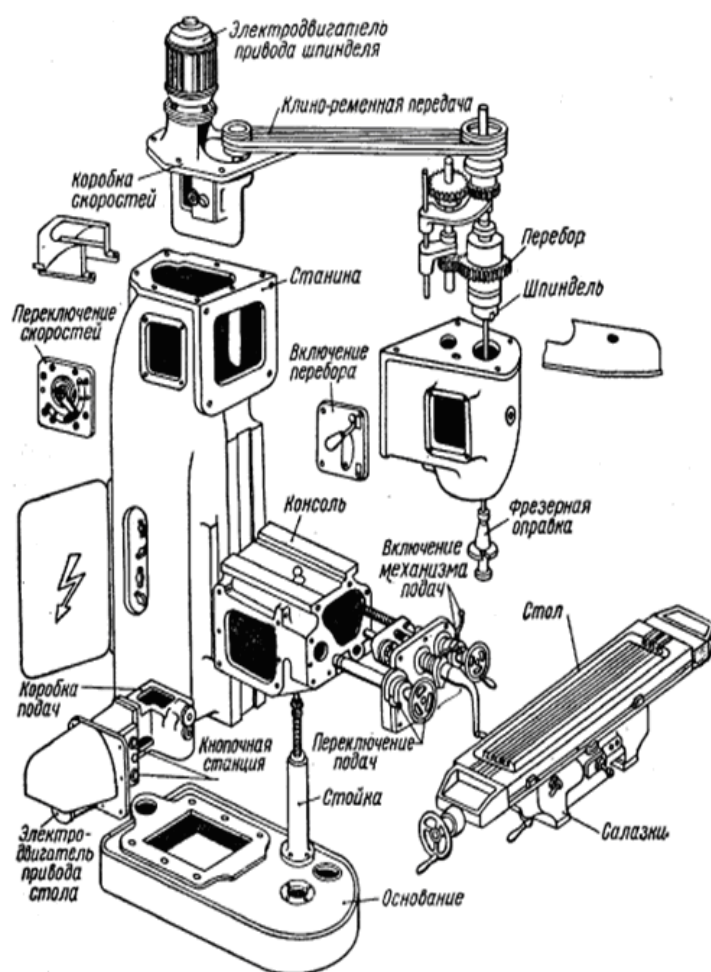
Основные узлы консольного вертикально-фрезерного станка 6М12П
